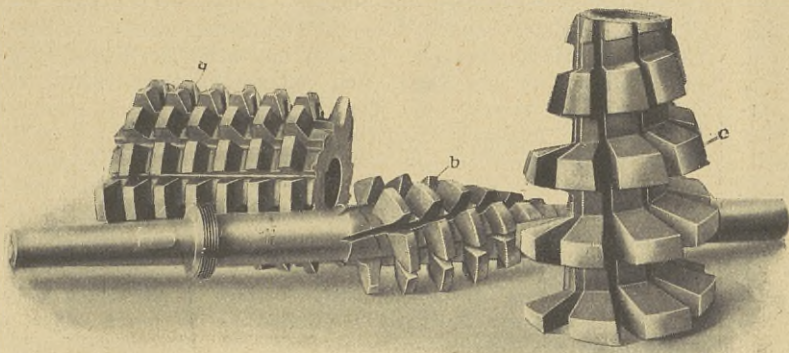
Eine Gruppe Abwälz- und Schneckenradfräser
